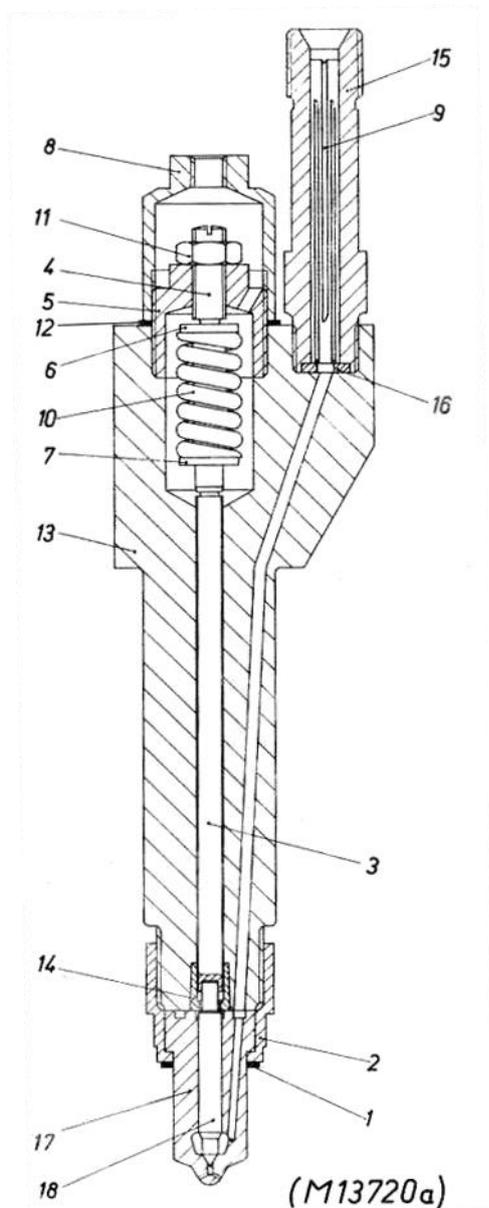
Форсунка двигателя NVD24 (Ч 17,5/24)
